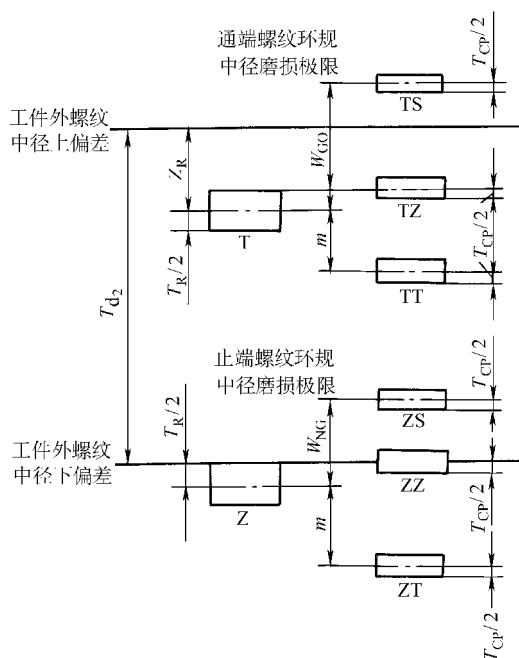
螺纹环规和校对螺纹塞规螺纹中径公差带
